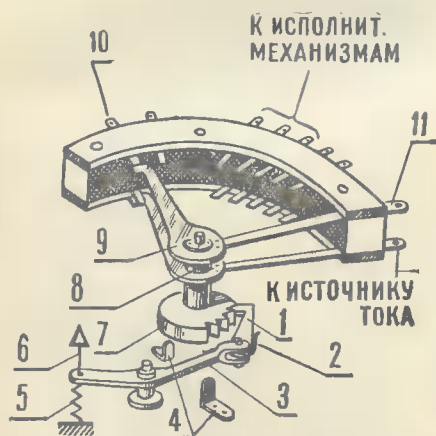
Блок подачи команд: 1 — храповый механизм; 2 — пружина; 3 — качалка; 4 — ограничитель хода; 5 — возвратная пружина; 6 — привод; 7 — храповое колесо; 8 — изоляторы; 9 — переключатели; 10 — контакты; 11 — контакты подачи питания и переключателям.
